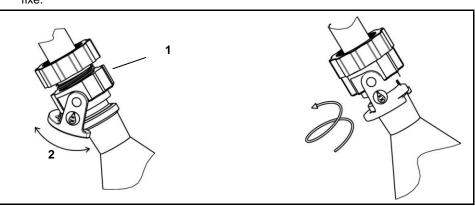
Collier de serrage (collier de serrage à axe pivotant)
